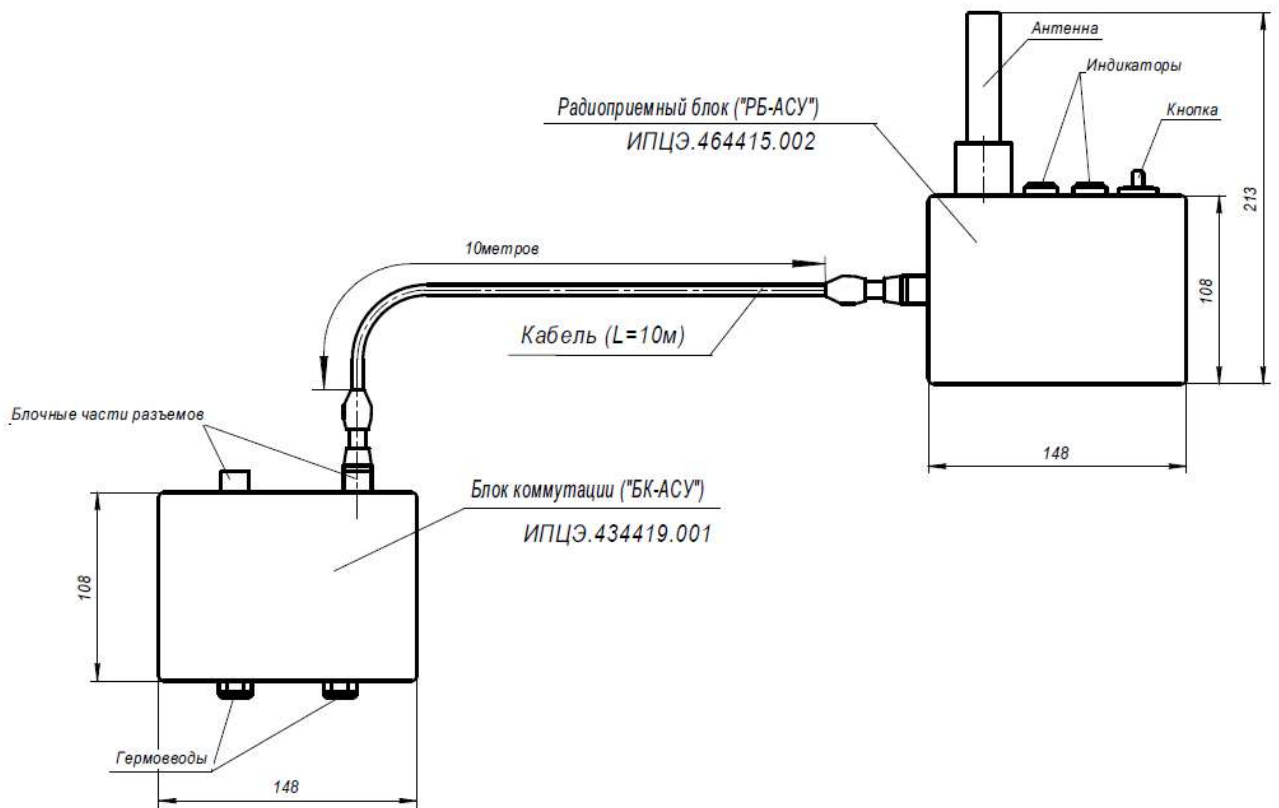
Габаритный чертеж устройства сопряжения «УС АСУ»
